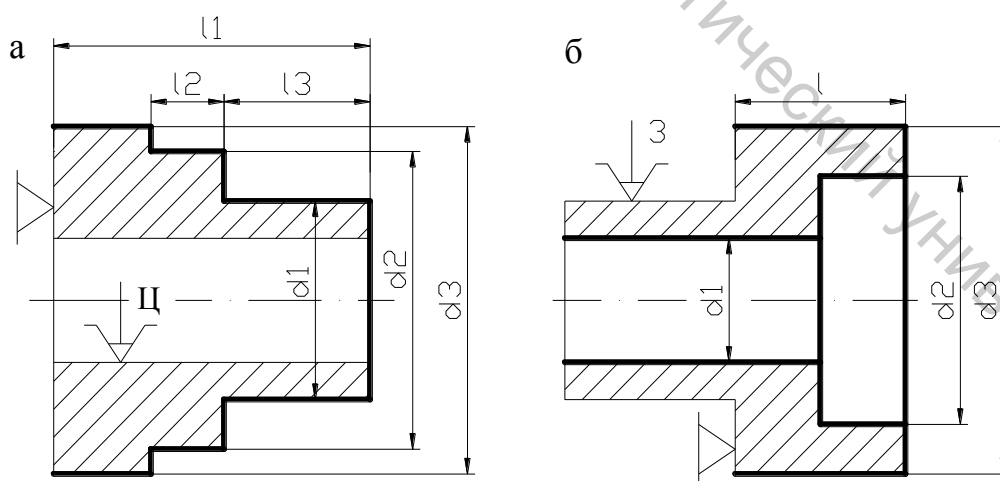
Схемы установки цилиндрических заготовок:
